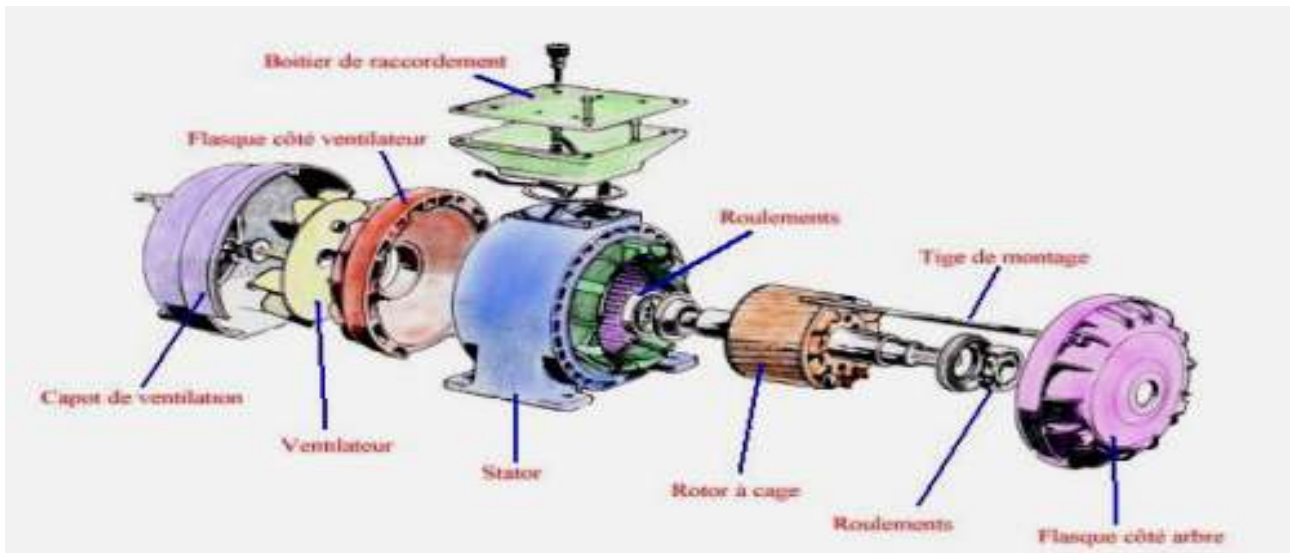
Moteur asynchrone triphasé rotor à cage [9].
